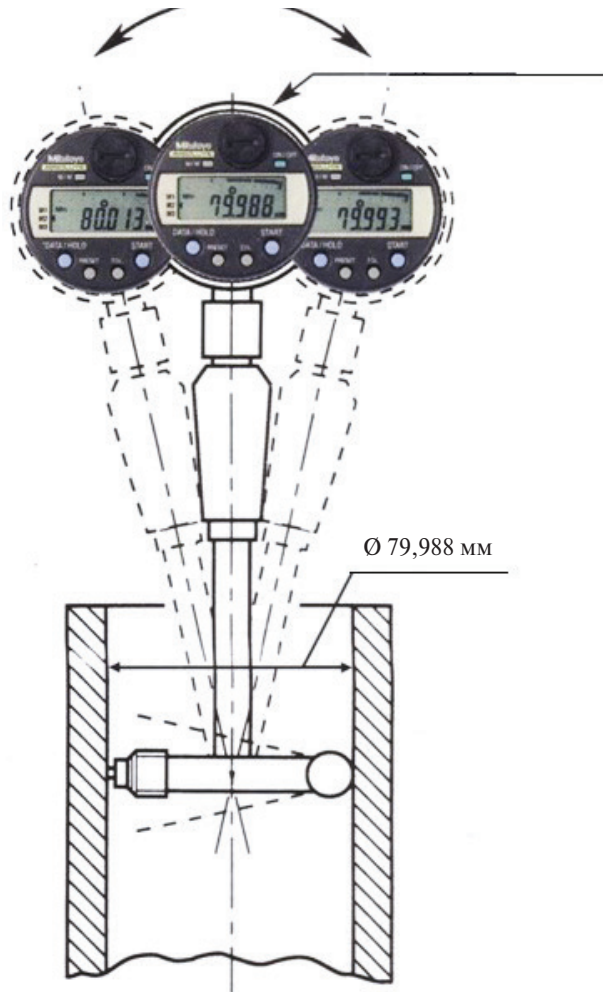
Контроль размера отверстия детали индикаторным нутромером [3]
